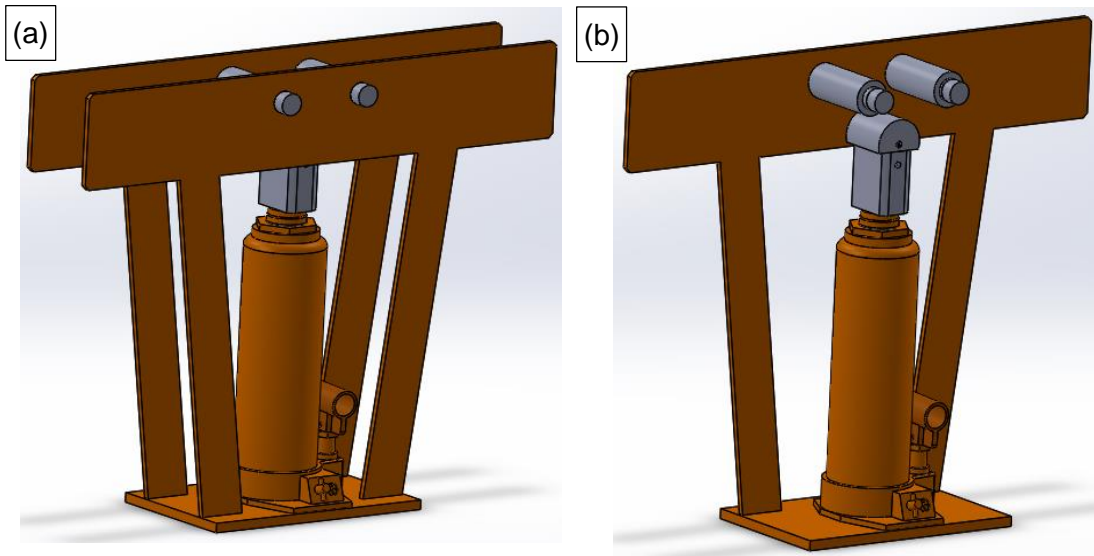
Prensa hidráulica y accesorios: (a) Con placa frontal y (b) Sin placa frontal.
